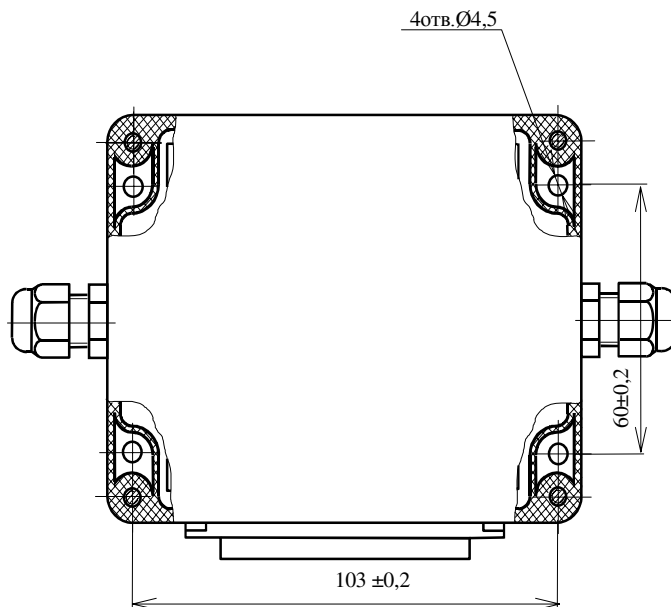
Присоединительные размеры корпуса адаптера АПС44
